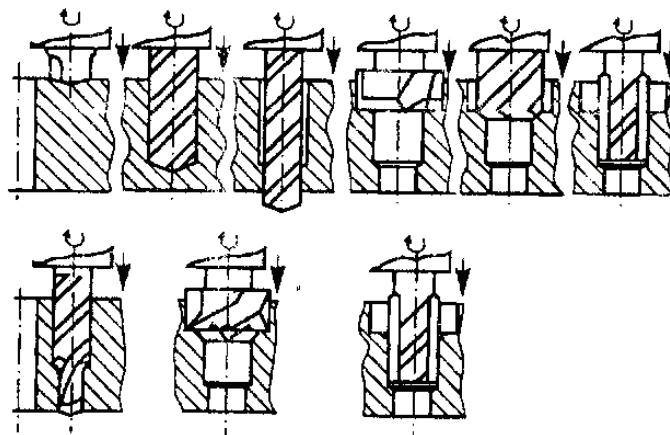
Можливі варіанти виготовлення модуля поверхонь базуючих 211
